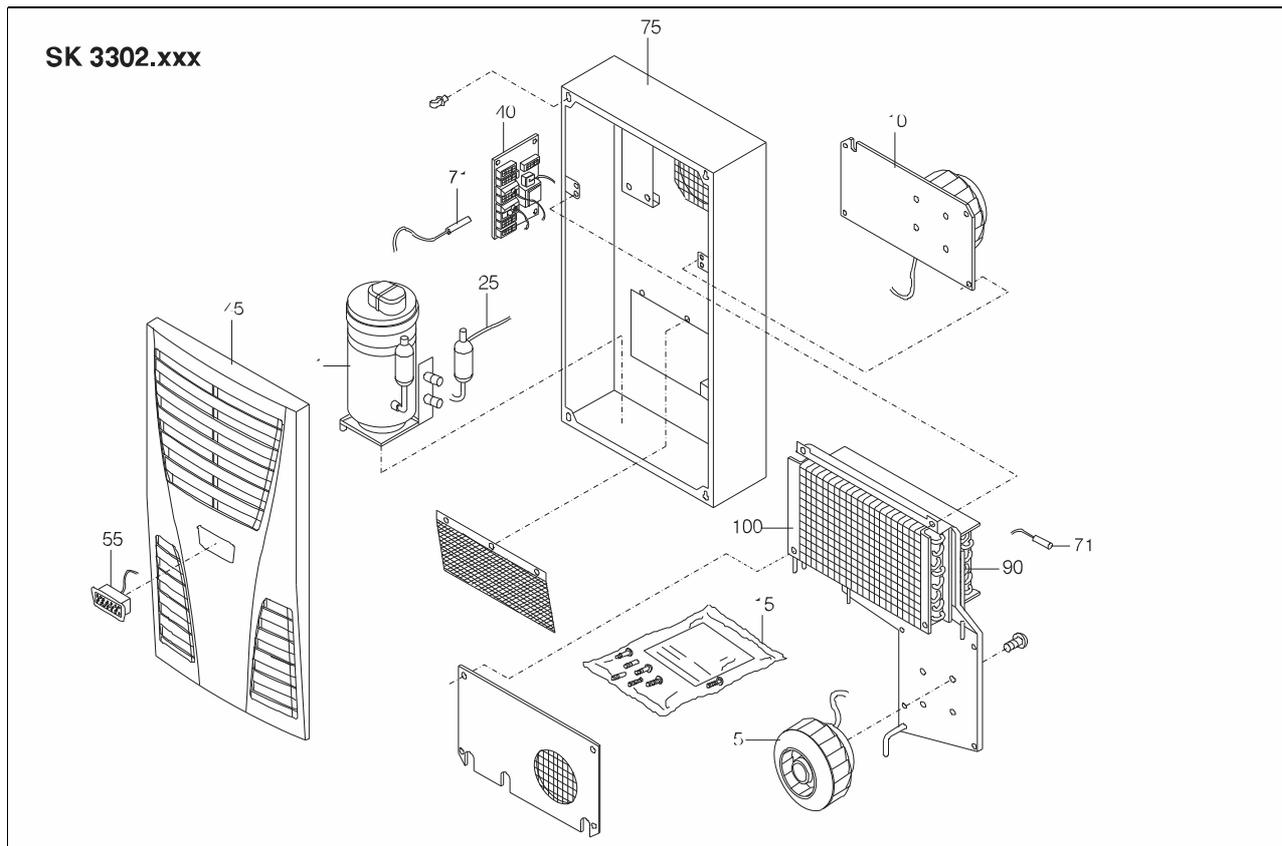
Pièces de rechange pour SK 3302.xxx
